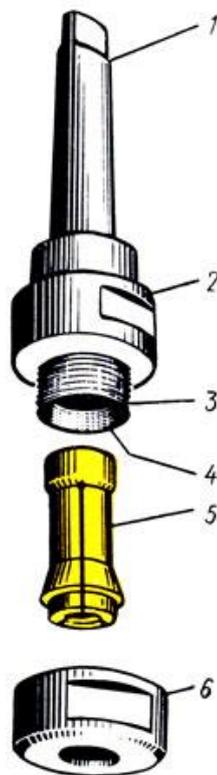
Цанговый патрон: 1 - хвостовик, 2 - корпус, 3 - резьбовая часть, 4 - корпус, 5 - цанга, 6 - гайка
